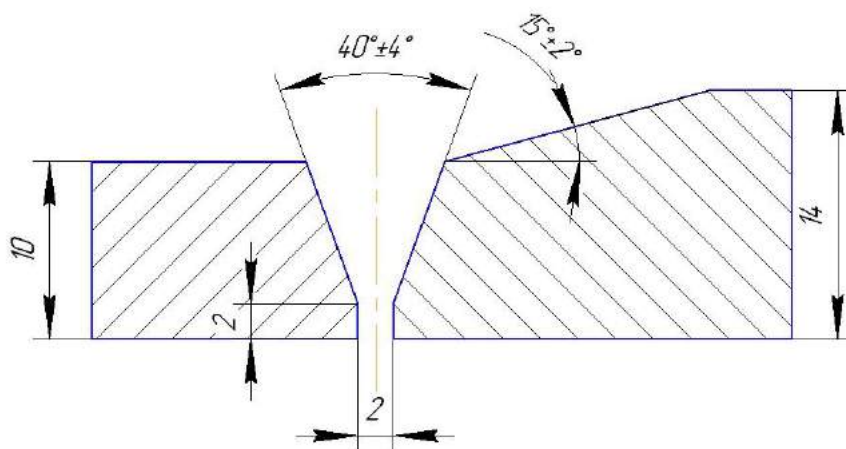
Эскиз стыкового сварного шва с разной толщиной листов (сварной шов № 2)
